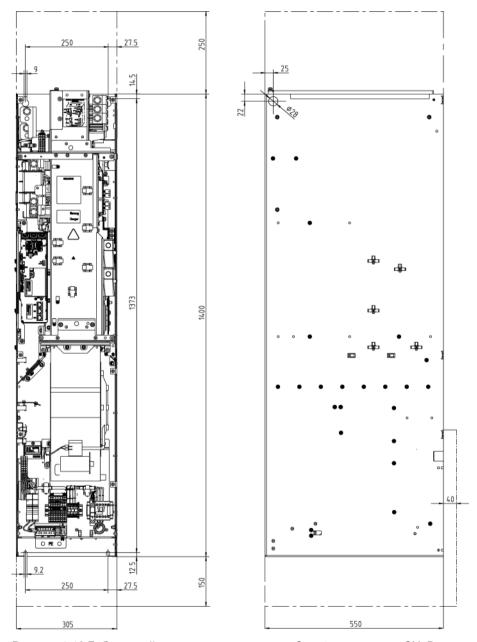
Габаритный чертеж модуля питания Smart, типоразмер GX. Вид спереди, вид сбоку
